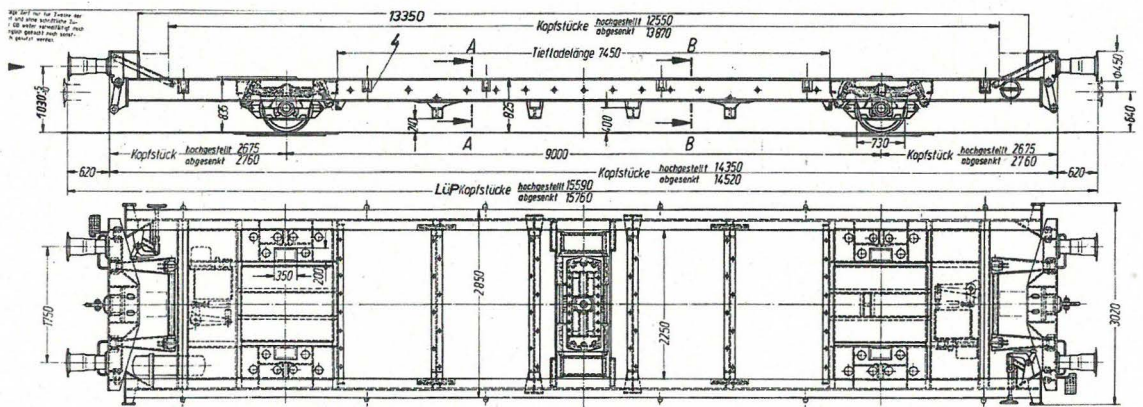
Zeichnung Gesamtansicht Fwg 635.01.000.002
